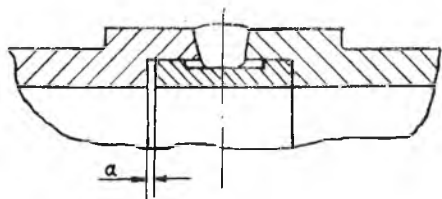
Сварные образцы труб из стали X18H10T. Свободная усадка — зазор  $a = 0,8 - 1,0$  мм. Задержанная усадка —  $a = 0$
